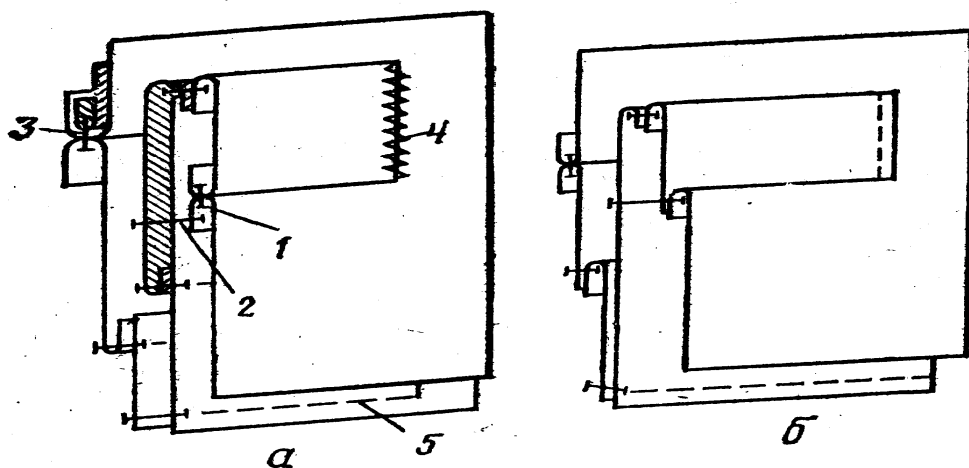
Сборочные схемы верхнего прорезного кармана с листочкой
